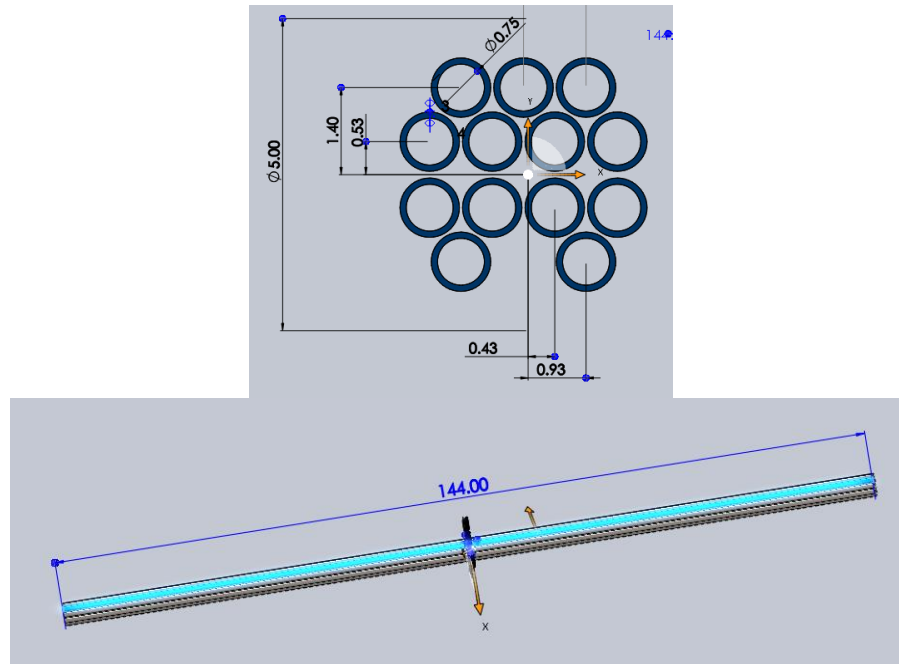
Dimensionamiento de los tubos del intercambiador de calor. Fuente: SolidWorks
